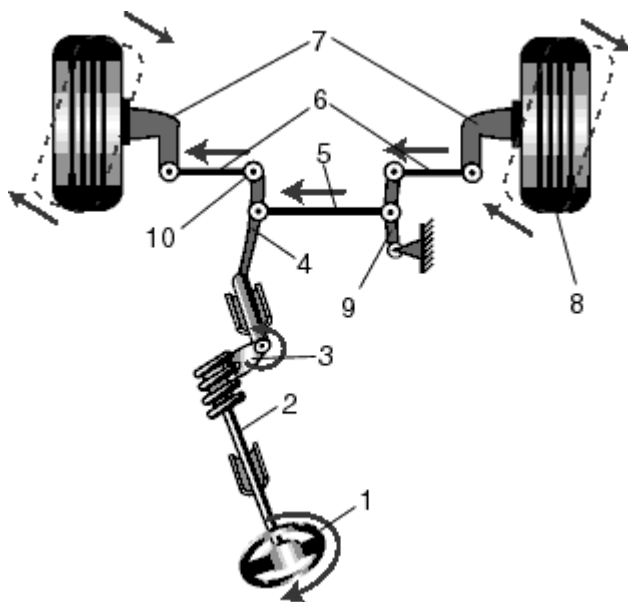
Схема рулевого управления с механизмом типа «червяк-ролик» 1 - рулевое колесо; 2 - рулевой вал с «червяком»; 3 - «ролик» с валом сошки; 4 - рулевая сошка; 5 - средняя тяга; 6 - боковые тяги; 7 - поворотные рычаги; 8 - передние колеса автомобиля; 9 - маятниковый рычаг; 10 - шарниры рулевых тяг
